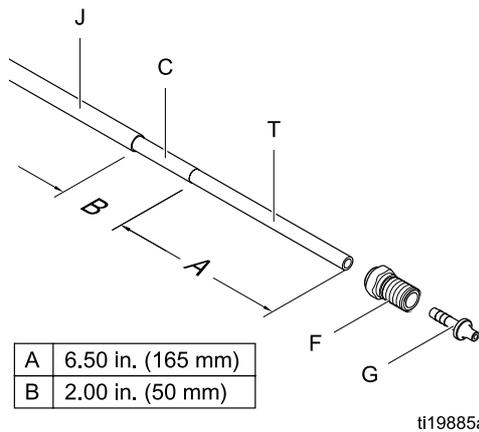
Abmessungen an Pistole für abgeschirmten Schlauch 24M732
